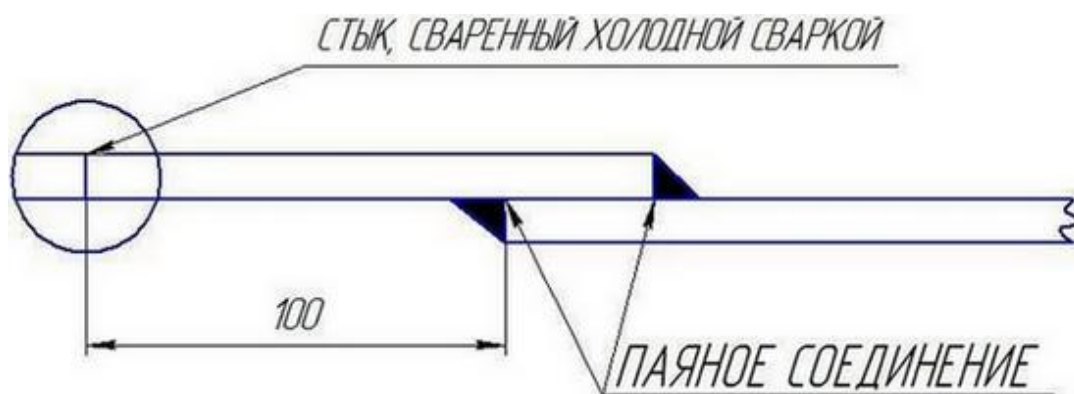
Расположение пайки относительно стыка холодной сварки
